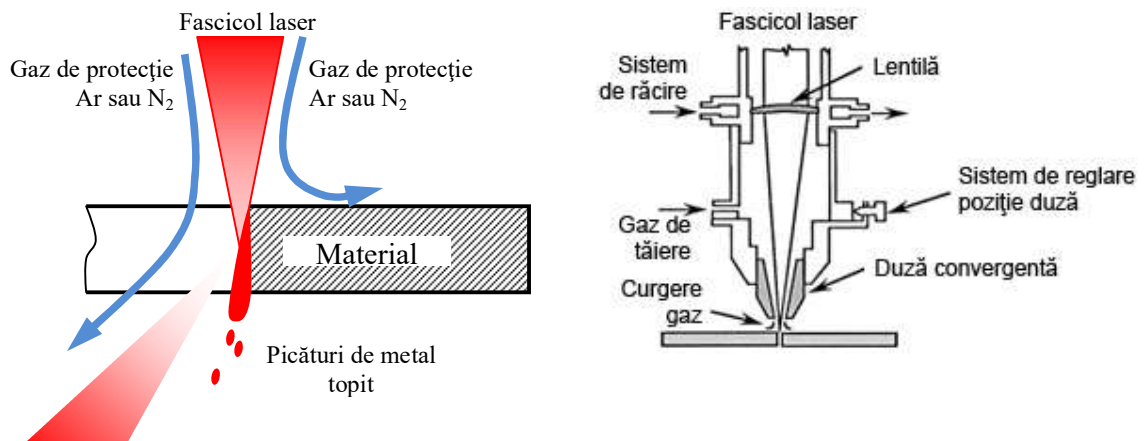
Principiul de tăiere prin topire cu laser.
